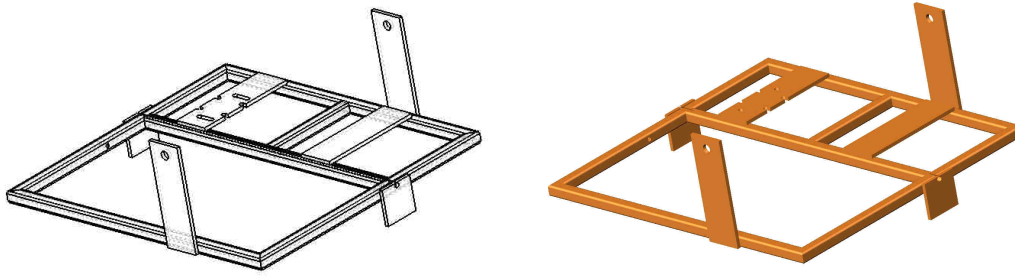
Diseño de base de basculación de la máquina de rotomoldeo.
